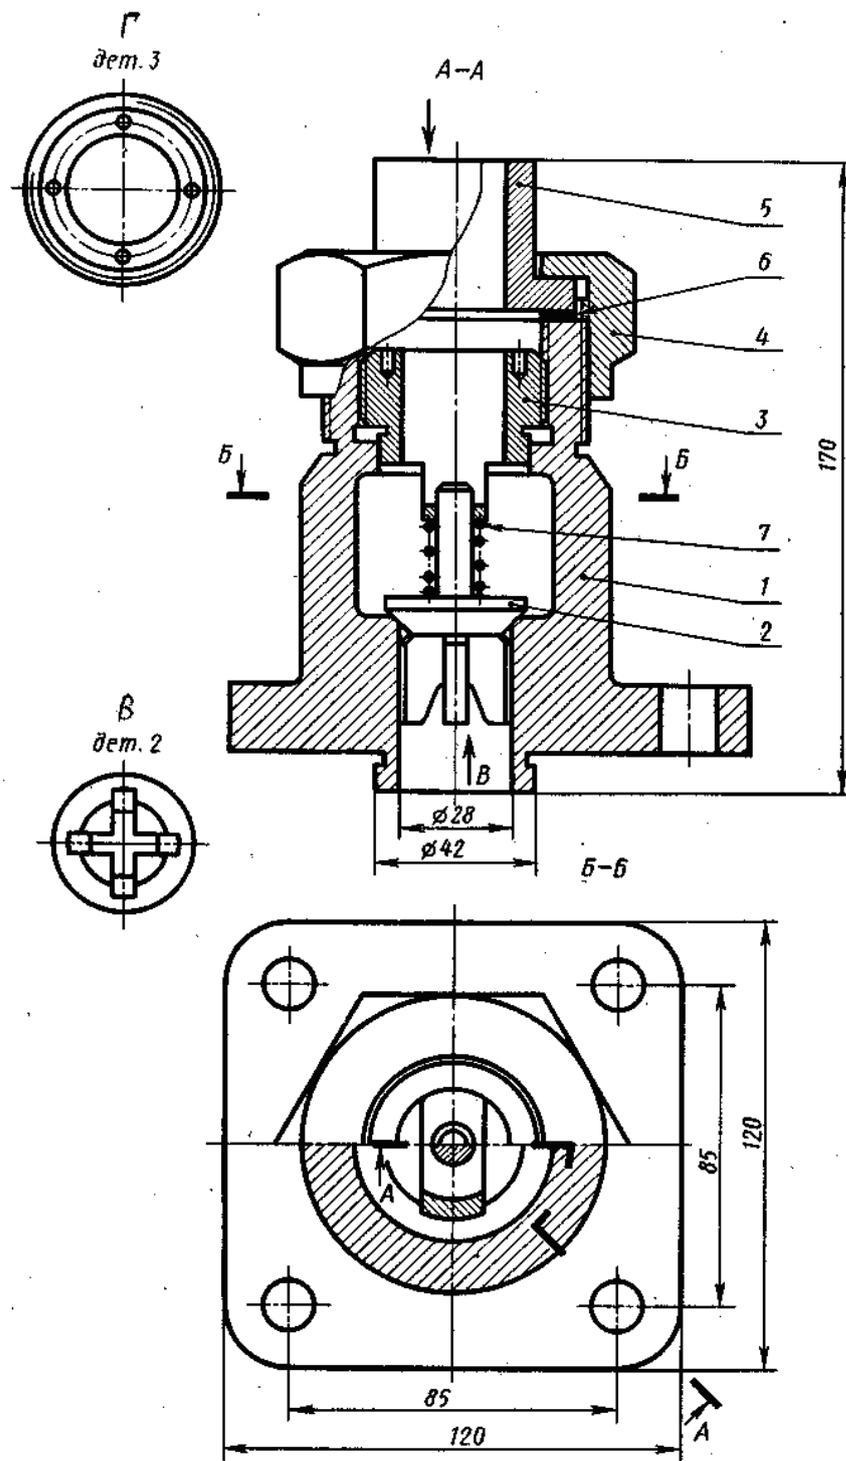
Сборочный чертеж сборочной единицы «Клапан обратный»
